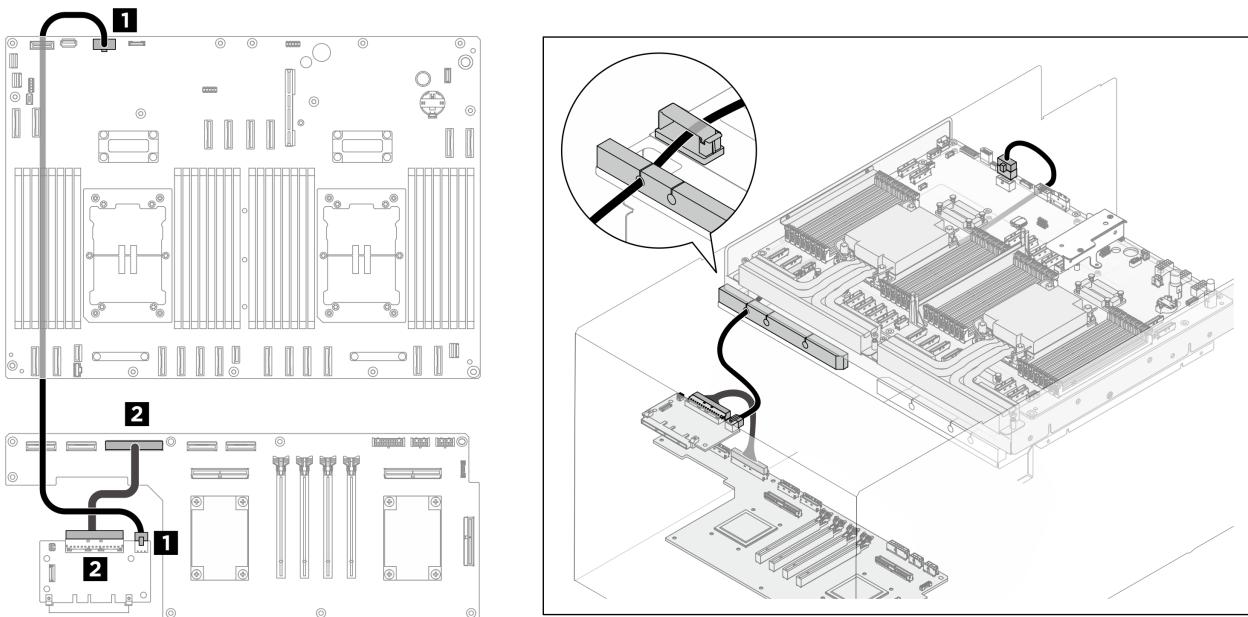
Instradamento dei cavi di alimentazione e di segnale
